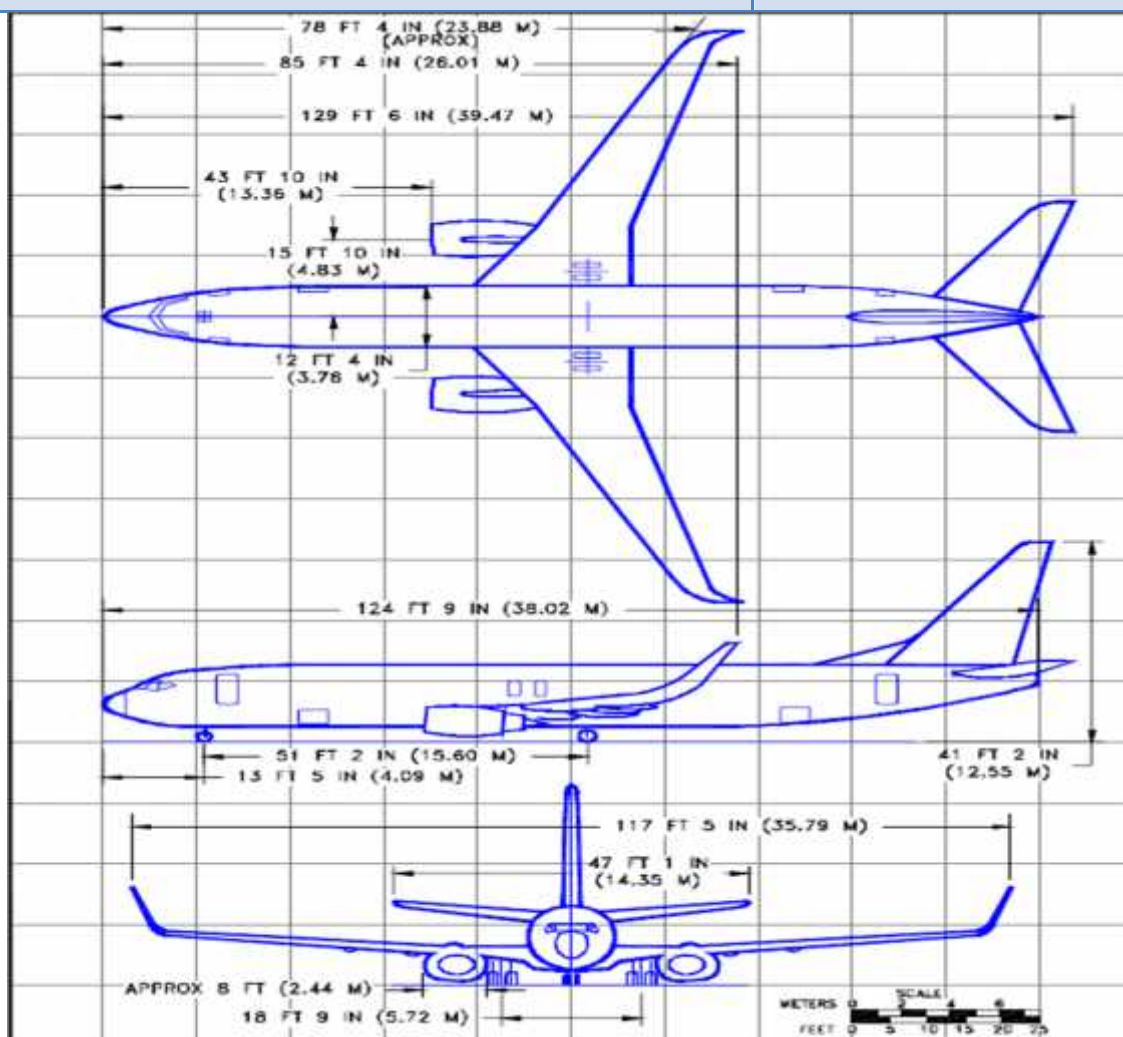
Arrangement générale et les premières dimensions pour une configuration avec Winglets B737-800
